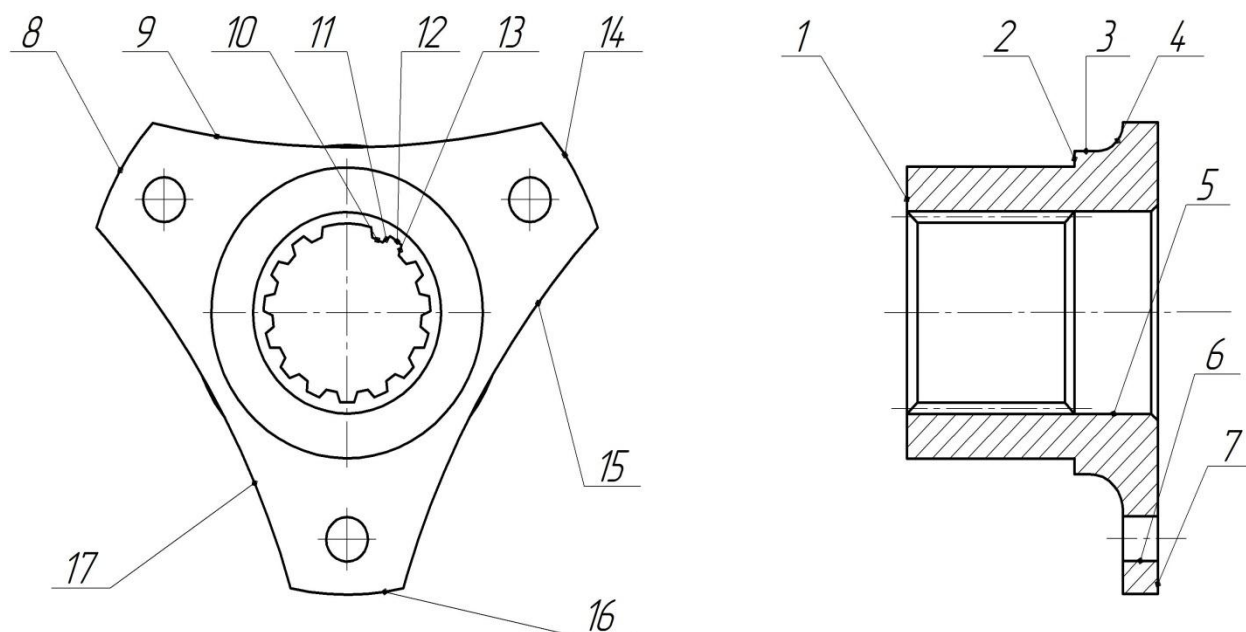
Деталь - «Ступица быстросъемная», общий вид
